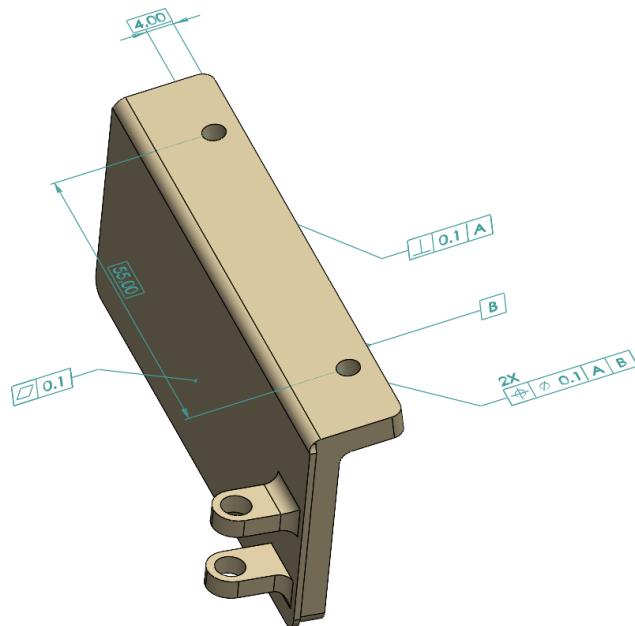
Tolerancias geométricas “Apoyo antebrazo_2”
